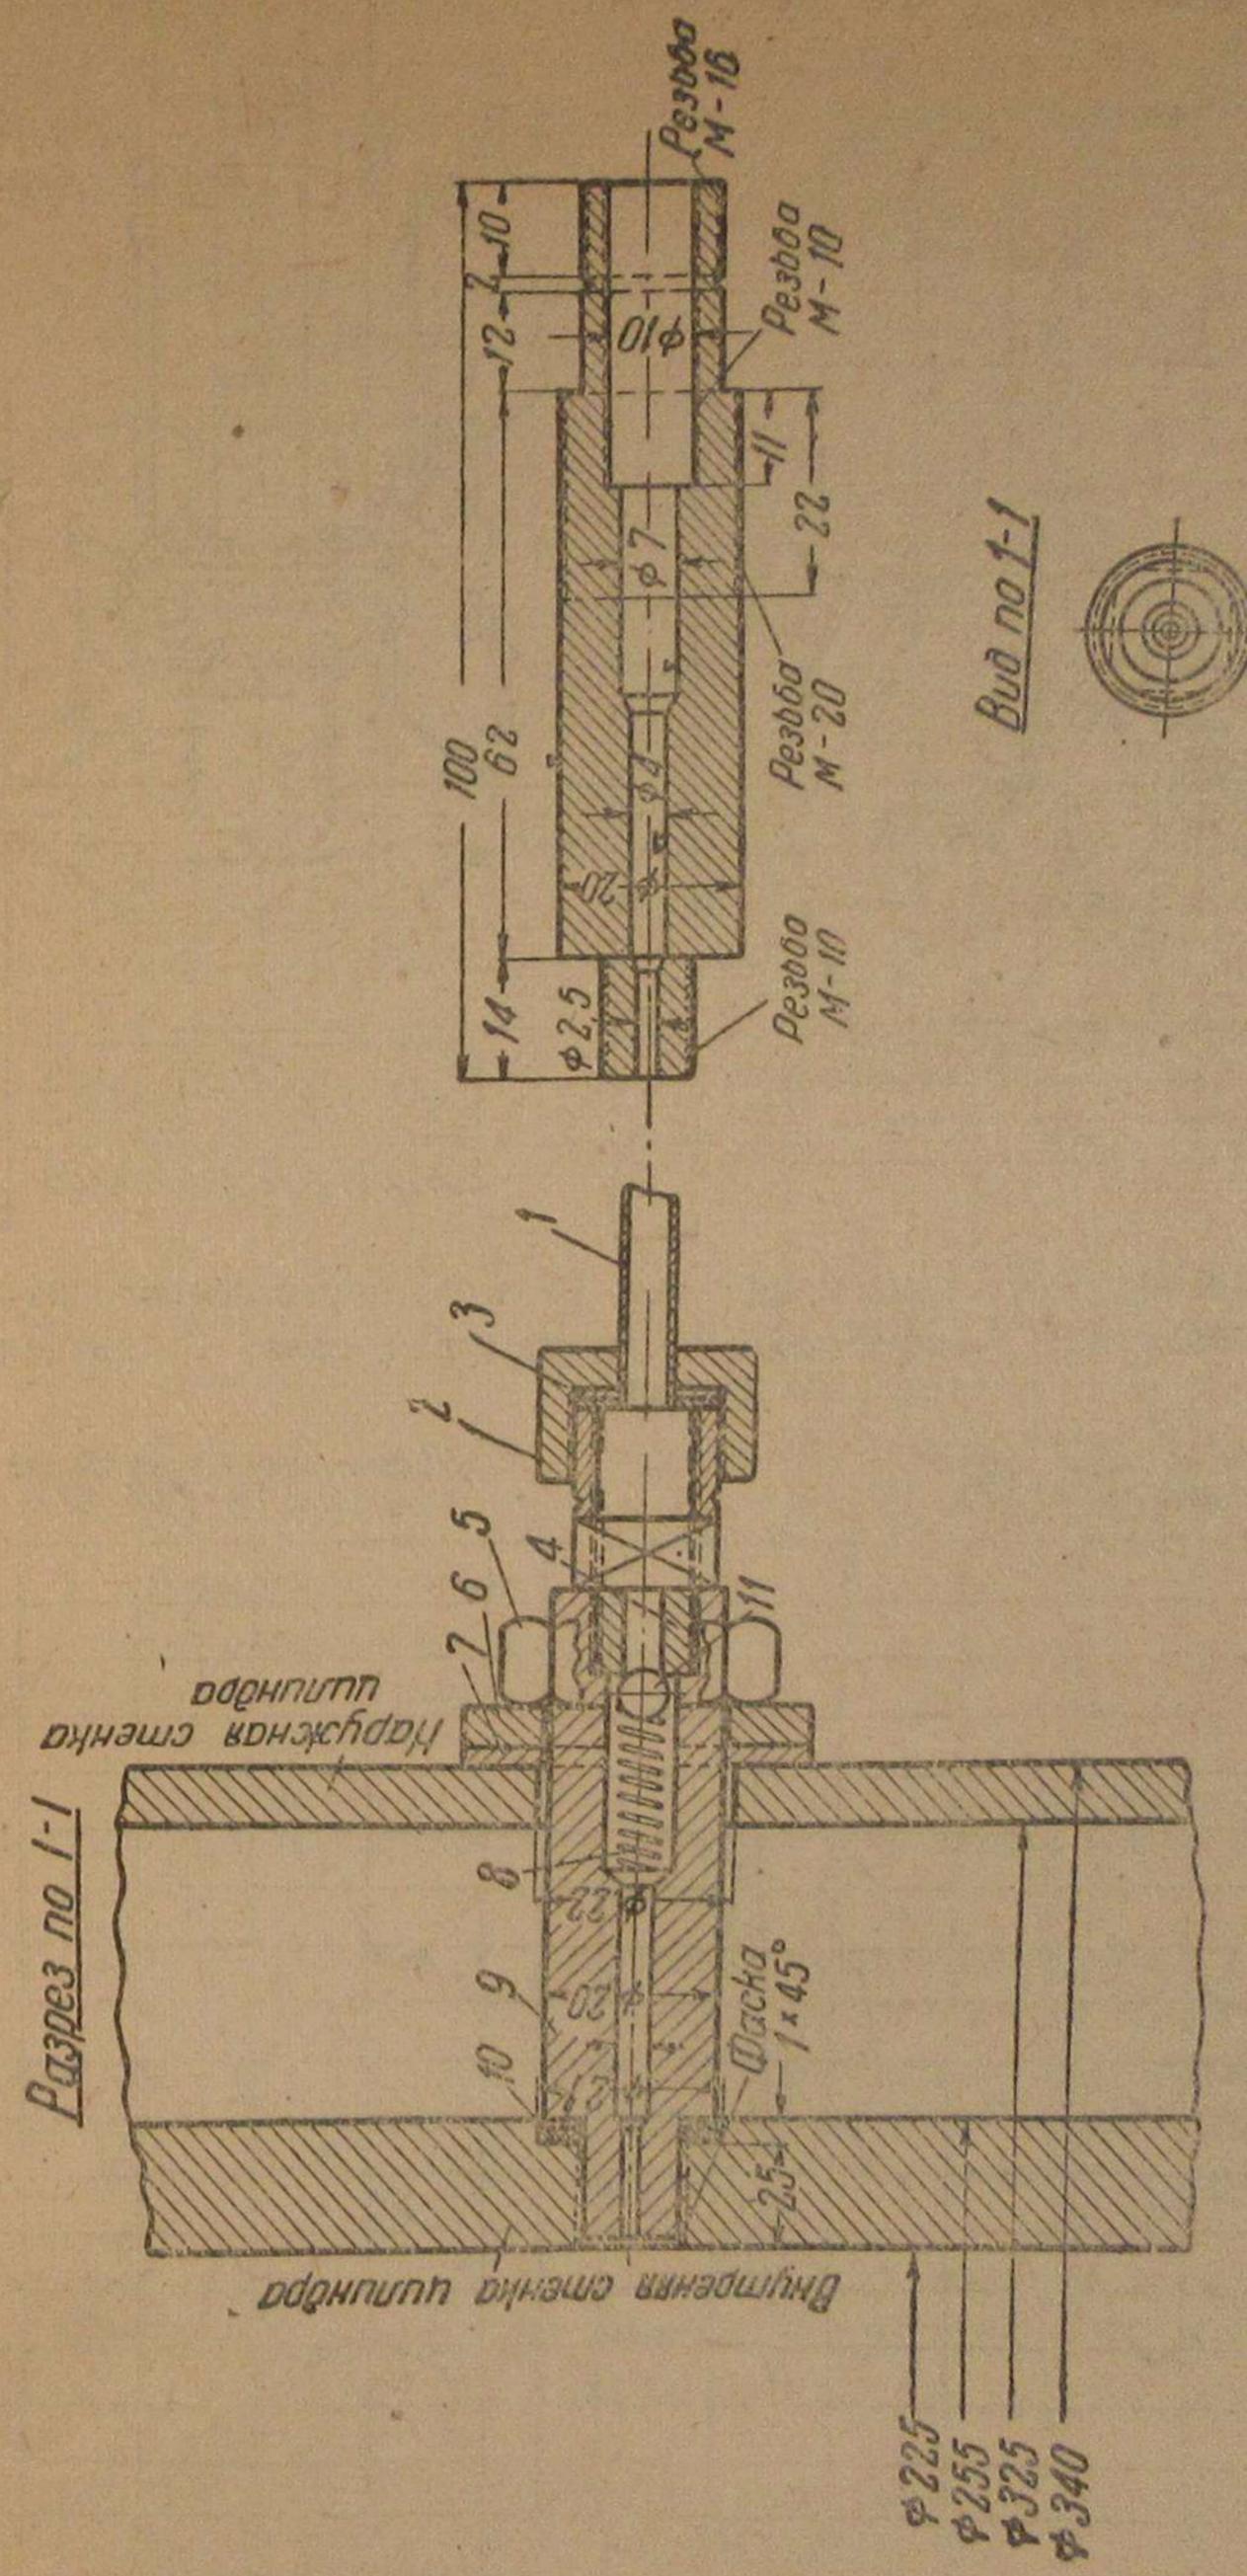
Штуцер для дополнительной смазки цилиндра двигателя мощностью 18 л. с.:
